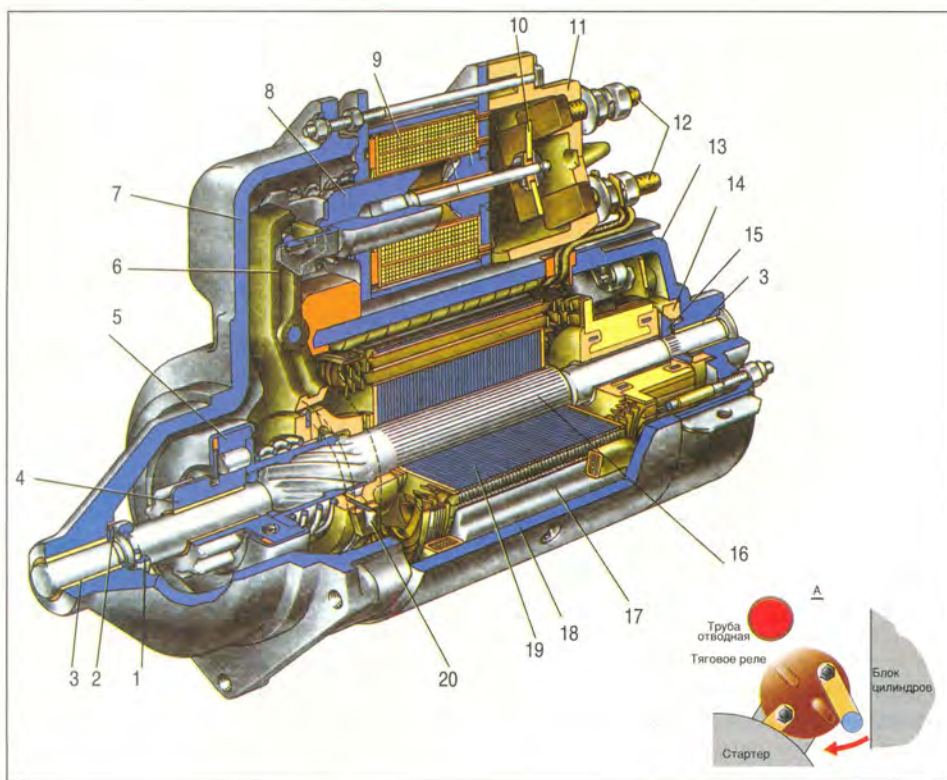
Конструкция стартера СТ-221: 1 – ограничительное кольцо; 2 – регулировочные шайбы; 3 – втулки; 4 – шестерня привода; 5 – обгонная муфта; 6 – двулучий рычаг; 7 – крышка со стороны привода; 8 – якорь реле; 9 – обмотка реле; 10 – контактная пластина; 11 – крышка реле; 12 – контактные болты; 13 – задняя крышка; 14 – тормозящее кольцо; 15 – коническое кольцо вала; 16 – вал якоря; 17 – полюс; 18 – корпус; 19 – якорь стартера; 20 – поводковое кольцо.
